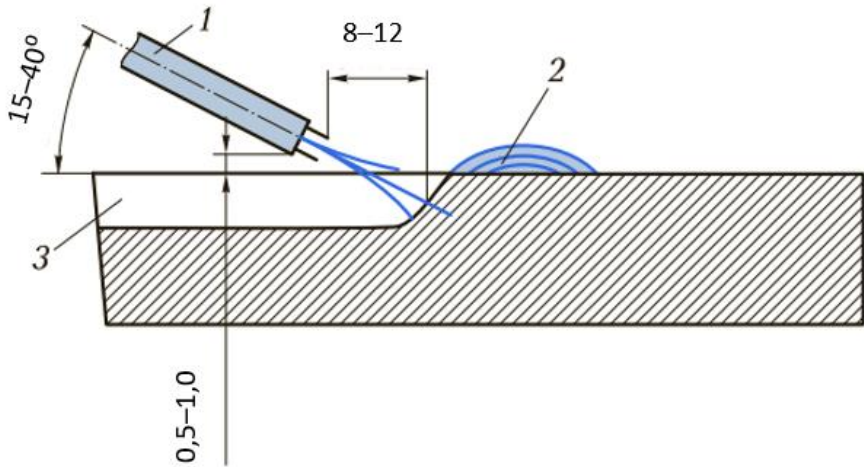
Схема поверхневого кисневого різання сталі:
